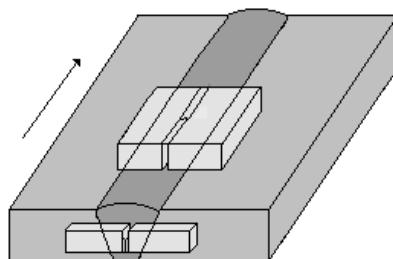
1. Desenho esquemático mostrando a posição de retirada dos corpos de prova em relação à junta soldada.
